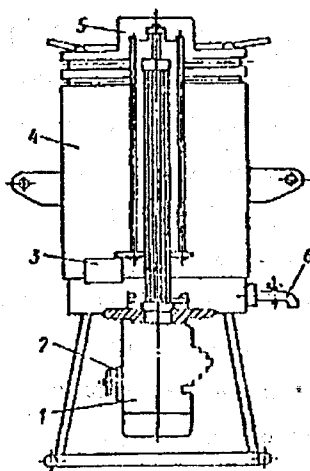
Змішувач СО-11: 1 - електродвигун; 2 - пакстний вимикач; 3 - редуктор; 4 - переносний бак; 5 - передавальний вал; 6 - кран зливний
